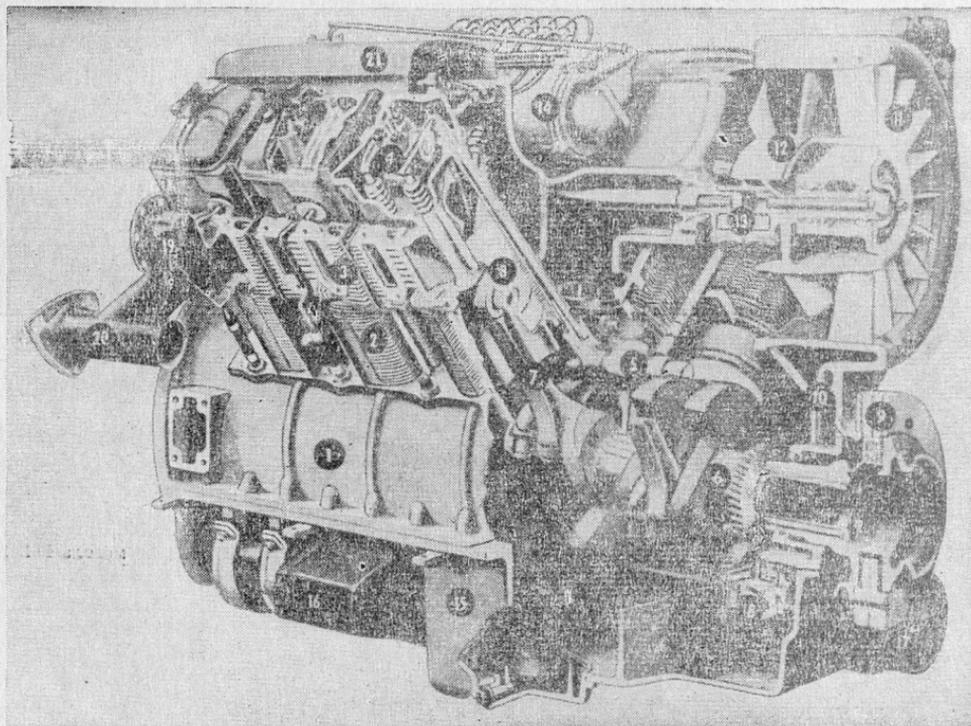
Продольный разрез V-образного дизеля с воздушным охлаждением Deutz:
